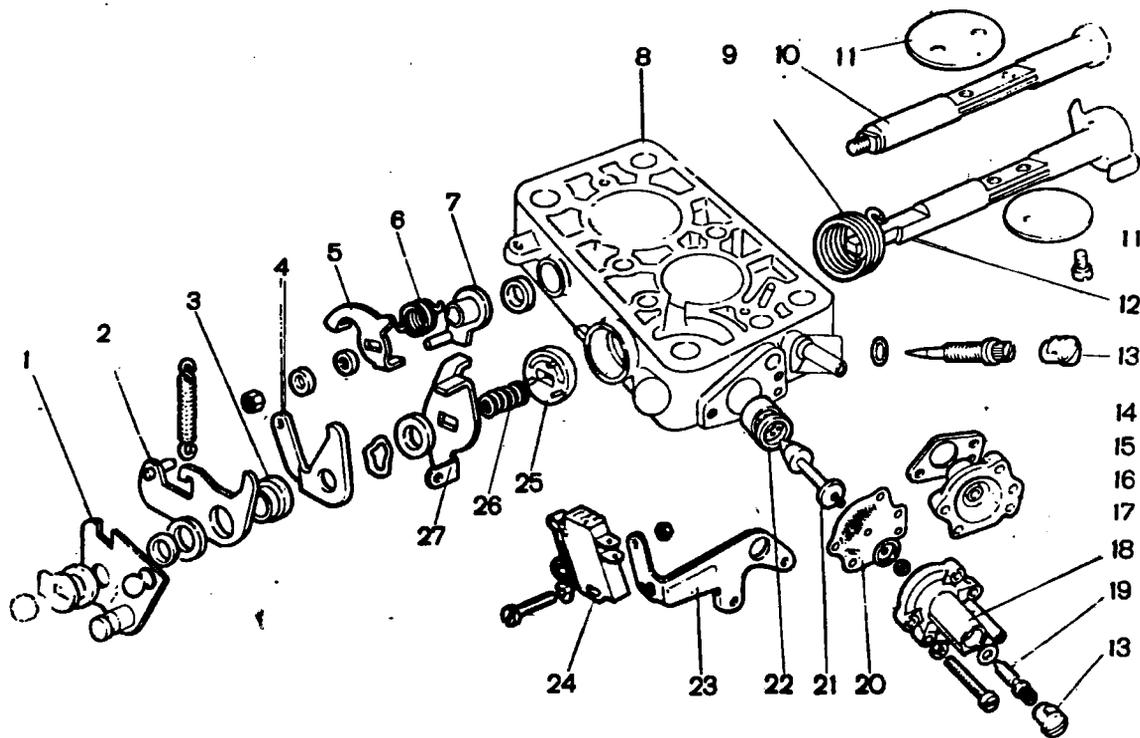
Детали корпуса дроссельных заслонок карбюратора 2107-1107010: 1 - рычаг привода дроссельных заслонок; 2 - рычаг, ограничивающий открытие дроссельной заслонки второй камеры; 3 - втулка; 4 - рычаг связи с воздушной заслонкой; 5 - рычаг, закрепленный на оси дроссельной заслонки второй камеры; 6 - пружина; 7 - рычаг, связанный с пневмоприводом; 8 - корпус дроссельных заслонок; 9 - возвратная пружина первой дроссельной заслонки; 10 - ось второй дроссельной заслонки; 11 - дроссельные заслонки; 12 - ось первичной дроссельной заслонки; 13 - ограничительные втулки; 14 - винт регулировки качества смеси холостого хода; 15 - уплотнительное кольцо; 16 - прокладка; 17 - корпус экономайзера принудительного холостого хода; 18 - крышка экономайзера; 19 - винт регулировки количества смеси холостого хода; 20 - диафрагма экономайзера; 21 - игла экономайзера; 22 - седло иглы; 23 - кронштейн крепления микропереключателя; 24 - микропереключатель; 25 - золотник; 26 - пружина золотника; 27 - рычаг, закрепленный на оси первой дроссельной заслонки
